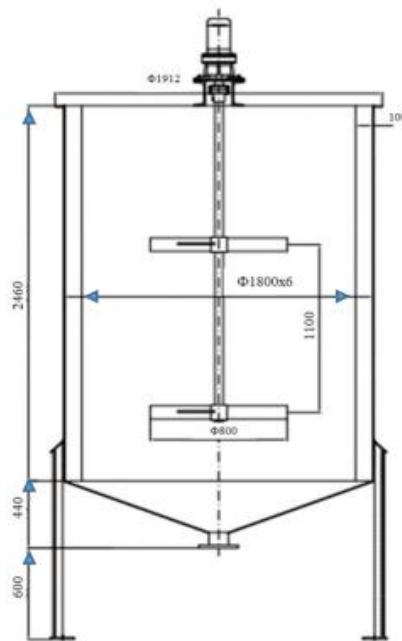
Чертеж реактора с механическим перемешивающим устройством
